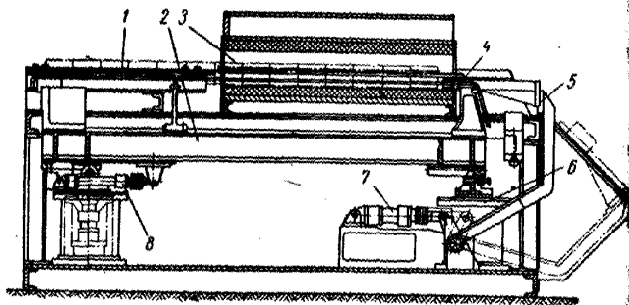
Схема нагревателя фирмы «АЕГ» (рис. 42):
